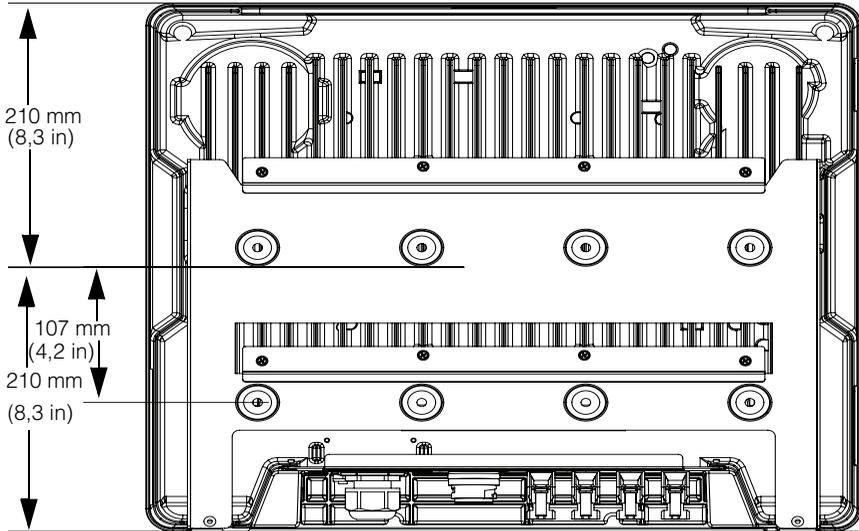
Emplacement du support de montage (vue arrière de l'onduleur)
